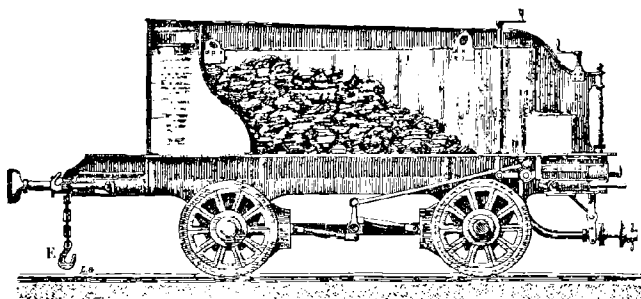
Le tender; coupe longitudinale; vue intérieure.
